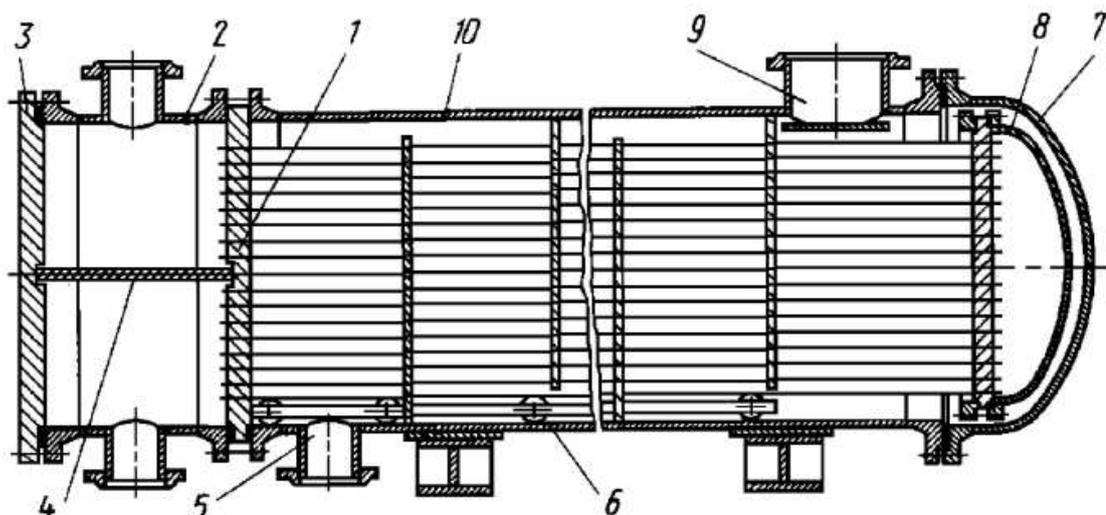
Горизонтальный двухходовой кожухотрубный конденсатор с плавающей головкой
